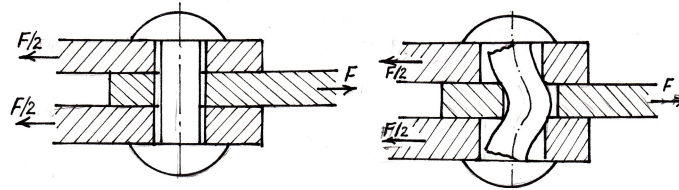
Rivet posé à froid : il faut que le rivet soit bien ajusté au trou, sous peine d'arrachement de sa tête.
